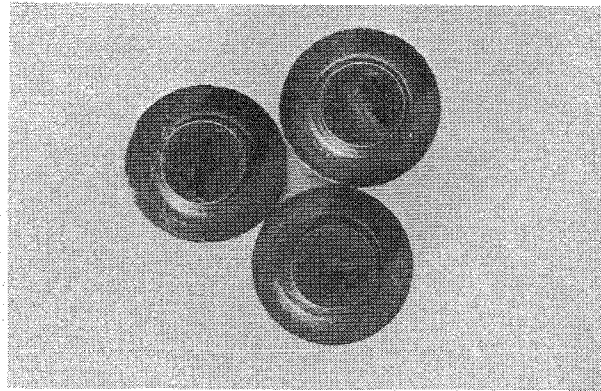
Partielle Aufschweißungen aus Colmonoy 6 auf Inconel 718
